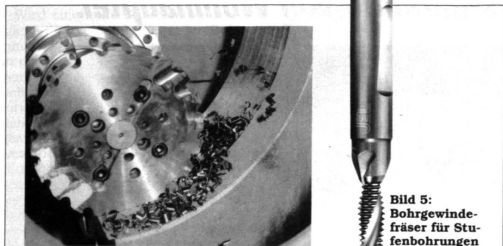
Schruppbearbeitung einer Bohrung mit Bohrzirkularfräser
